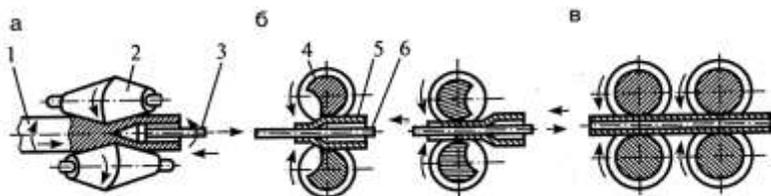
Схема прокатки бесшовных труб на трубопрокатной установке с пилигримовым станом: а – прошивной стан; б – пилигримовый стан; в – калибровочный стан; 1 – заготовка; 2 – валки; 3 – игла; 4 – рабочие валки пилигримового стана; 5 – заготовка; 6 – заготовка с оправкой; 7 – калибровочные валки
